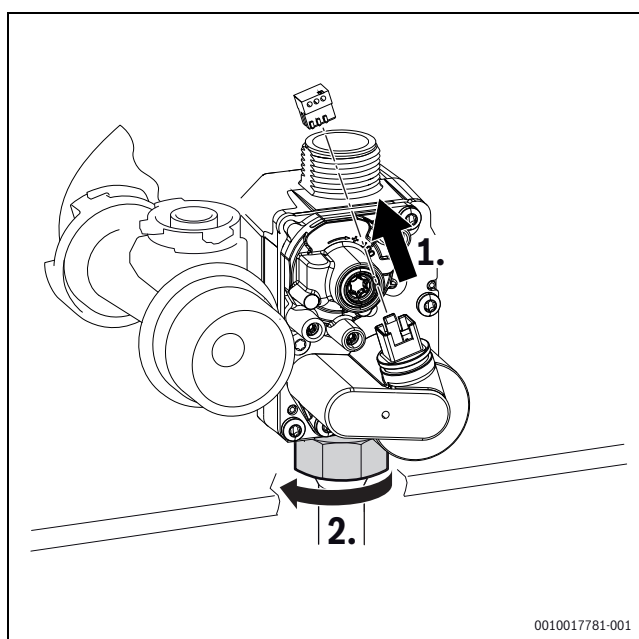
Retirer le connecteur et desserrer l'écrou-raccord
